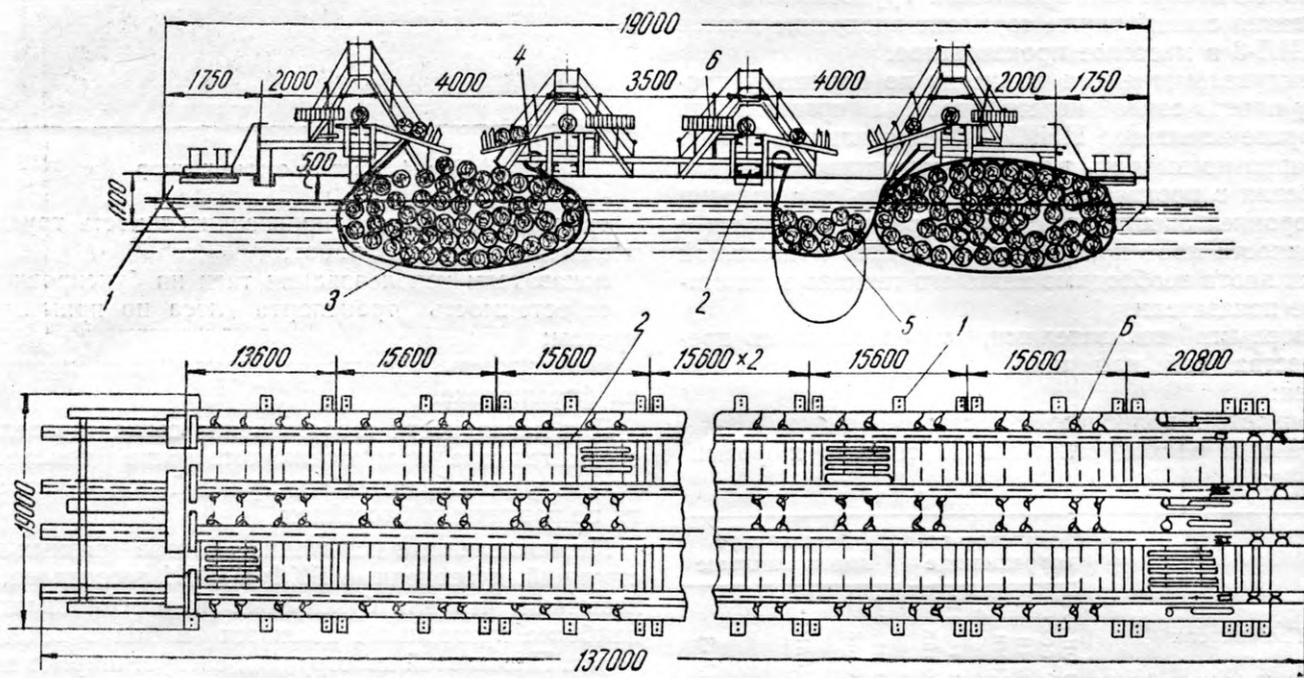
Схема сортировочно-сплоточного агрегата ВКФ-7:
